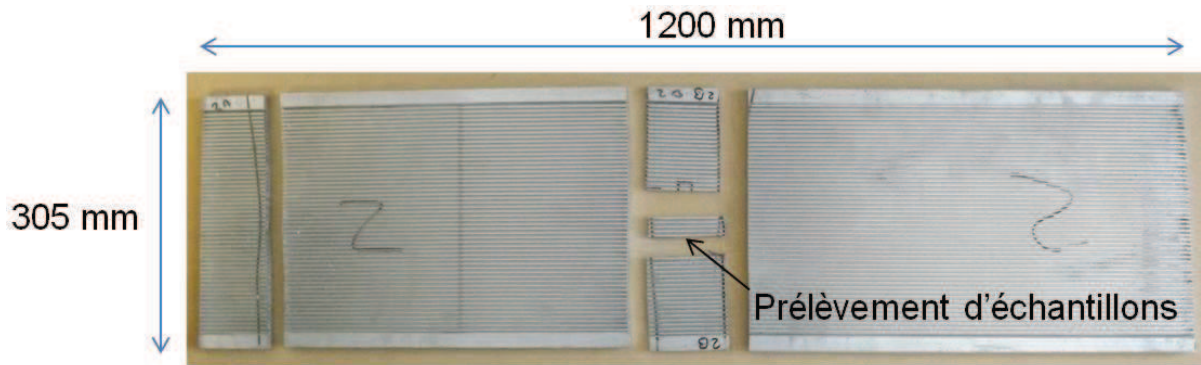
Vue de dessus d'une maquette industrielle découpée en vue du prélèvement d'échantillons
